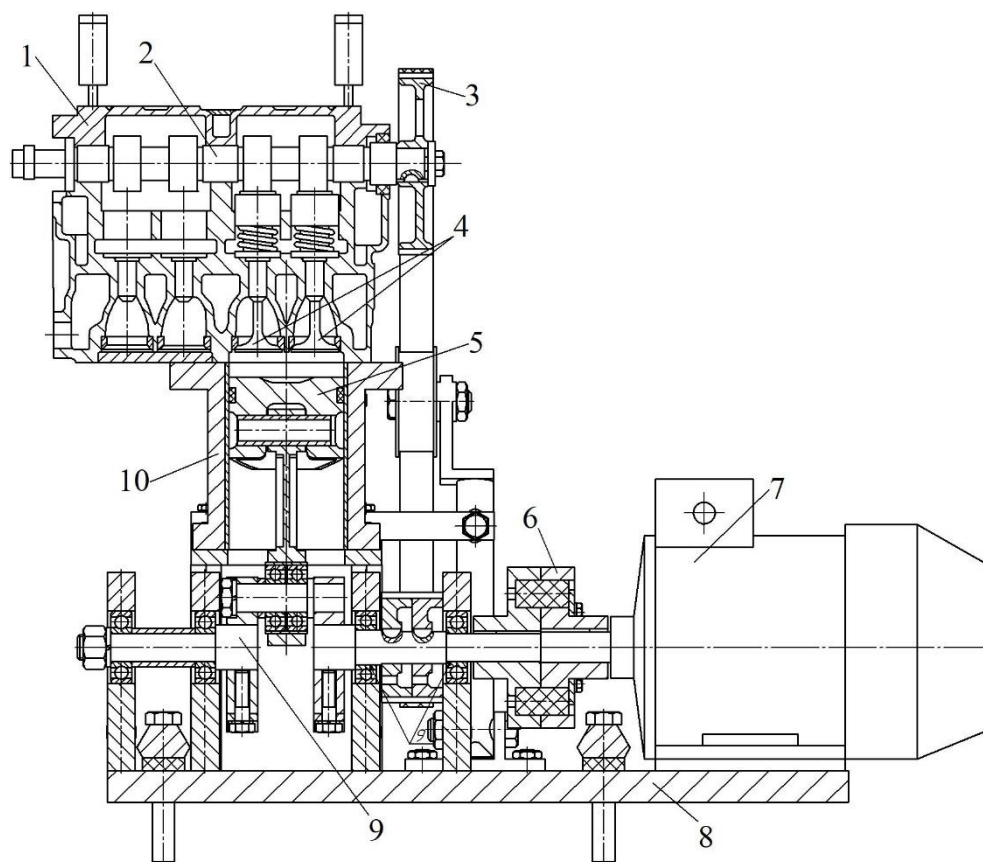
Продольный разрез одноцилиндровой модели поршневого двигателя внутреннего сгорания: 1 – головка блока; 2 – распределительный вал; 3 – шкив привода распредвала; 4 – впускной и выпускной клапаны; 5 – поршень; 6 – муфта соединения коленвала и вала электродвигателя; 7 – асинхронный двигатель; 8 – основание; 9 – сборный коленчатый вал; 10 – цилиндр
